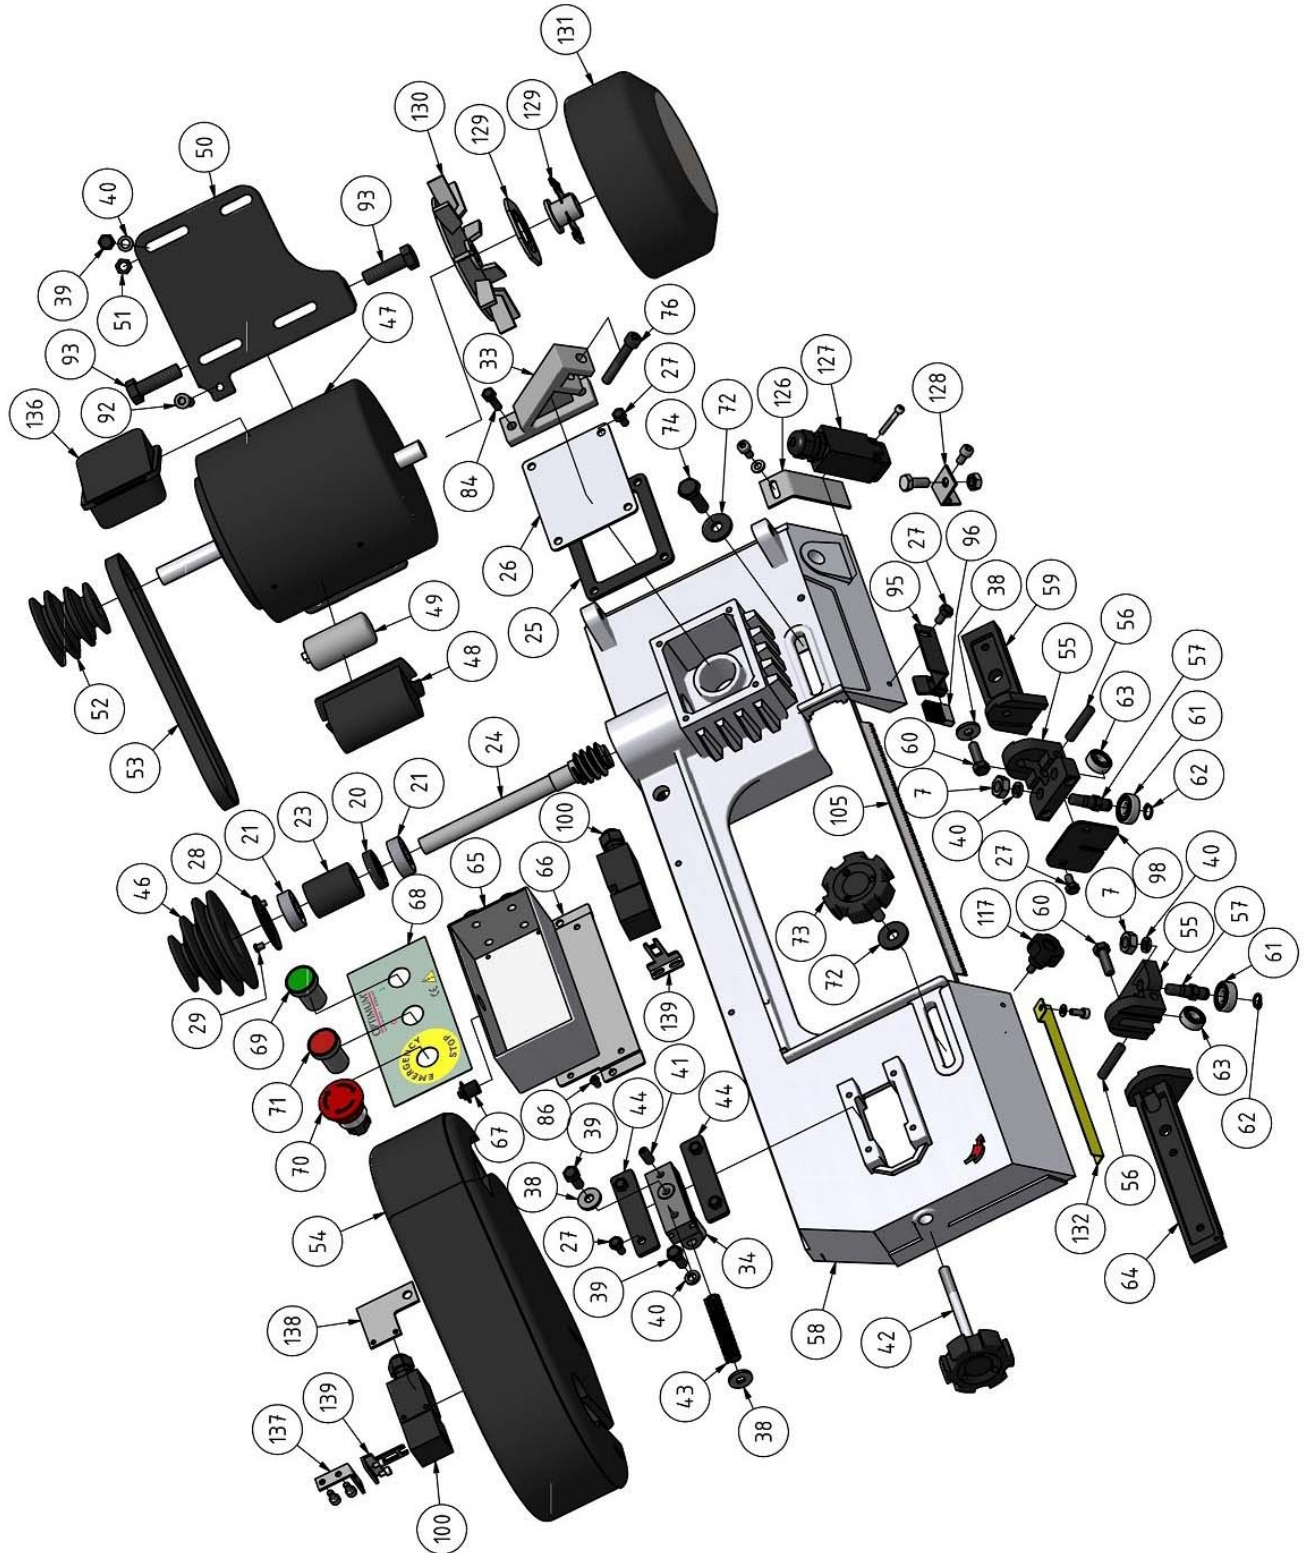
Ersatzteilzeichnung 1 von 4 - Parts drawing 1 of 4
